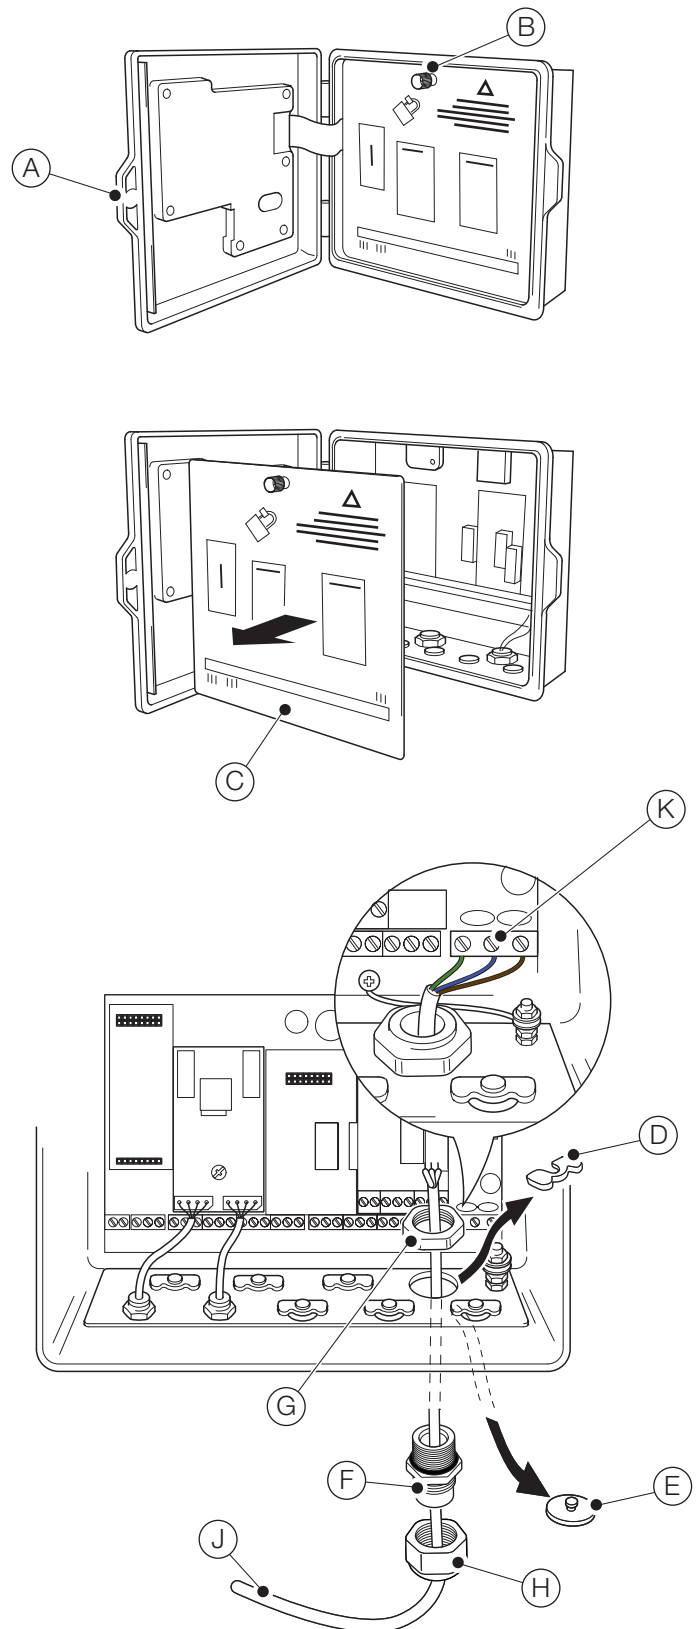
Anschließen der Messumformer-Stromversorgung
